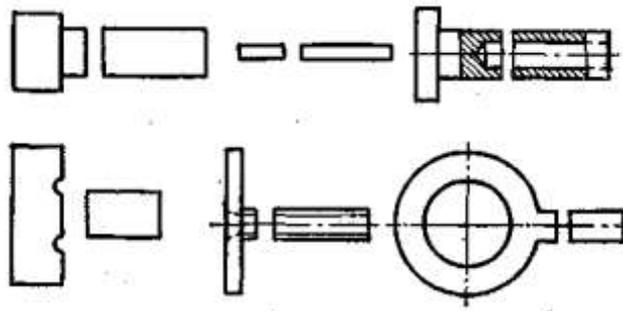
Типы сварных соединений, выполняемых стыковой.
